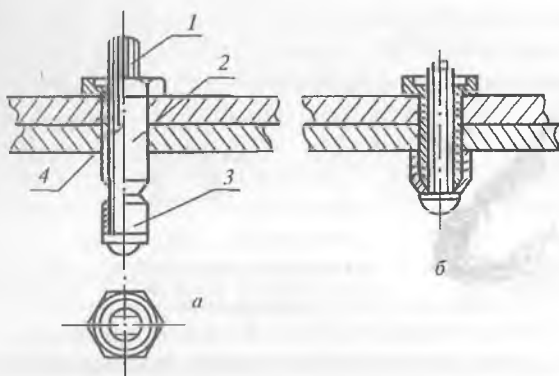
Заклепка с высоким сопротивлением срезу для односторонней клепки: а — конструкция заклепки; б — установленная заклепка; 1 — винт; 2 — корпус; 3 — кольцо; 4 — выточка в винте
